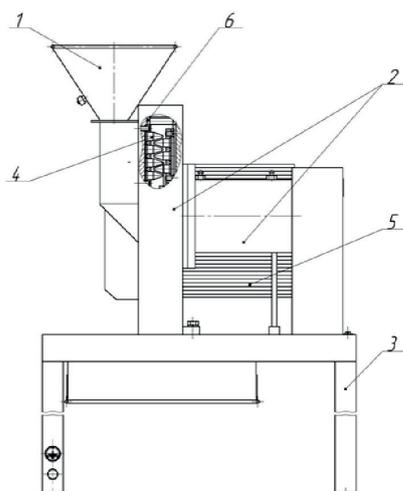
Дробилка Ш12-ДСК: 1 — загрузочный бункер; 2 — корпус; 3 — опора;
